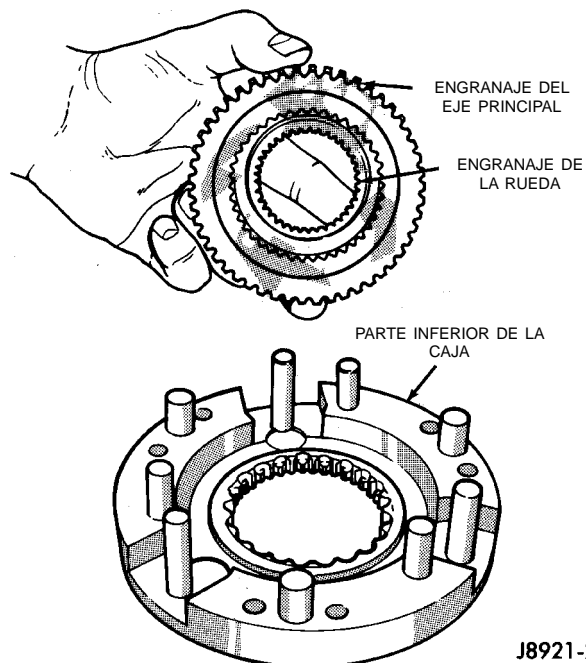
Desmontaje de engranajes planetarios y arandela de empuje
